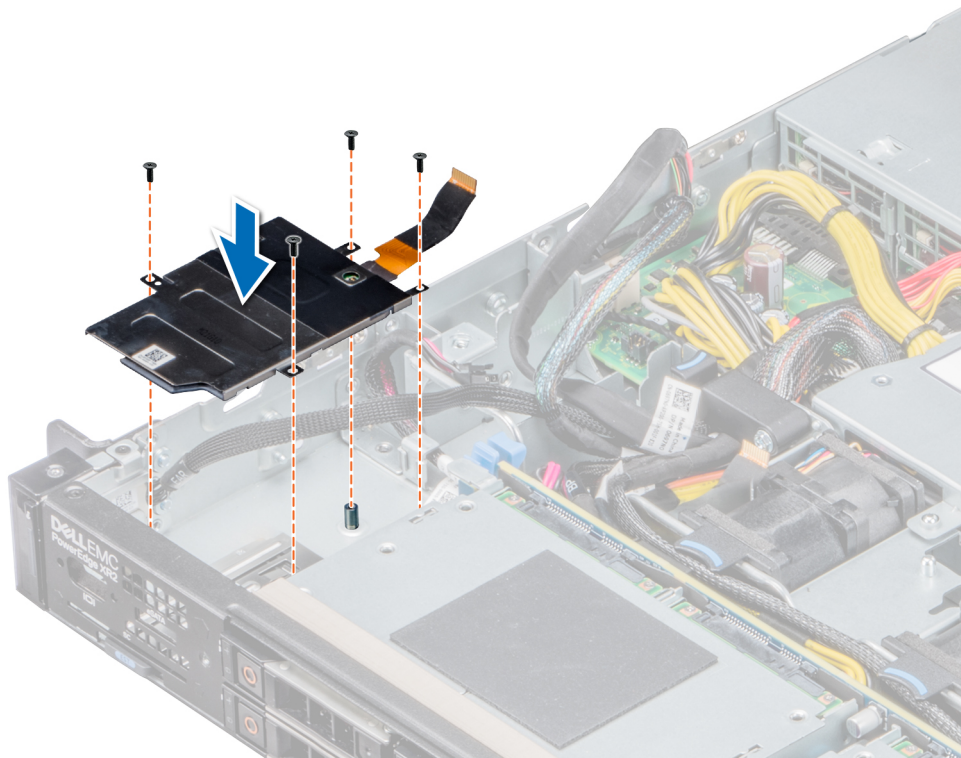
Einbauen des Smart Card-Lesegeräts
